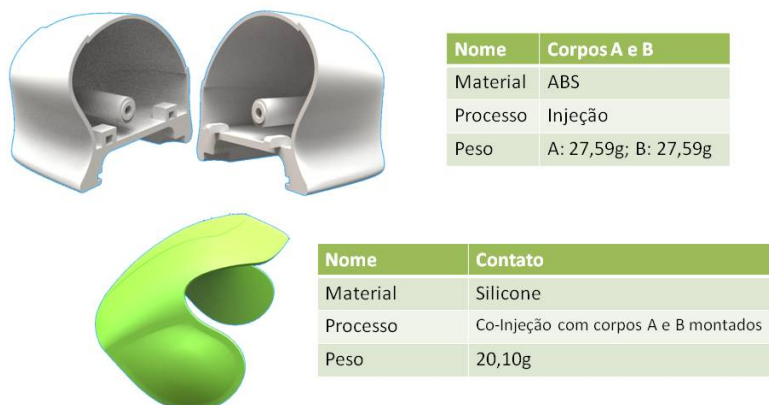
Ex. de detalhamento técnico do produto - vista explodida
